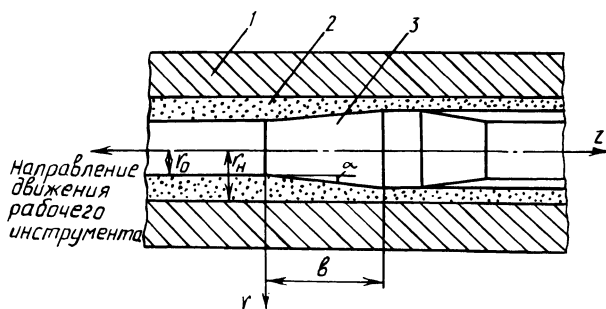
Схема калибрования пористой трубчатой заготовки по внутреннему диаметру:
